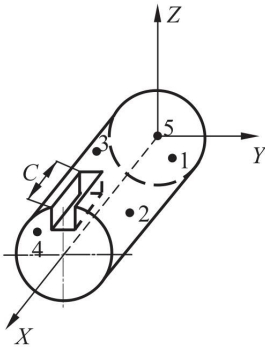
Установка заготовки з позбавленням п'яти ступенів свободи
